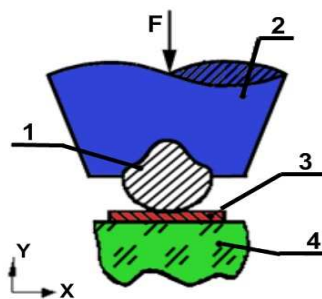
Схема УЗ сварки: 1–проволока; 2–сварочный инструмент; 3–контактная площадка; 4–кристалл
